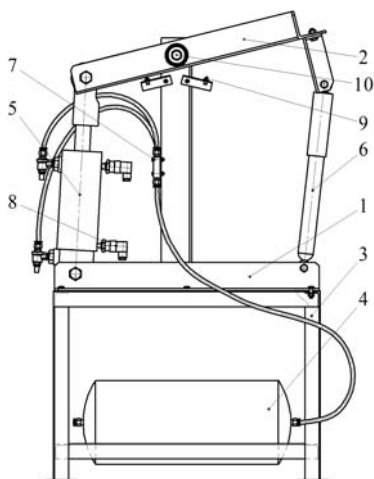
Стенд для испытания амортизаторов: 1 – рама; 2 – качающаяся поперечина; 3 – подставка; 4 – ресивер; 5 – пневмоцилиндр; 6 – амортизатор; 7 – распределитель; 8 – датчик давления; 9 – концевые выключатели; 10 – датчик угла поворота.
